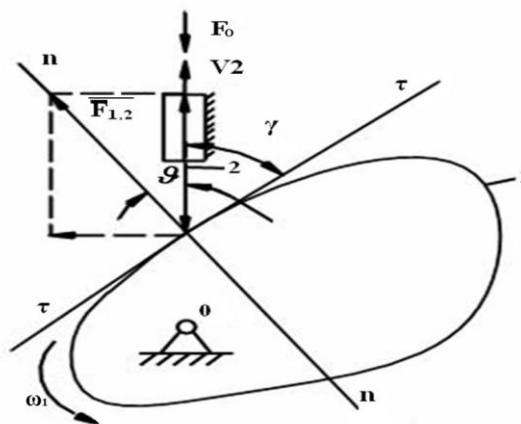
Кулачковий механізм з загостреним штовхачем
